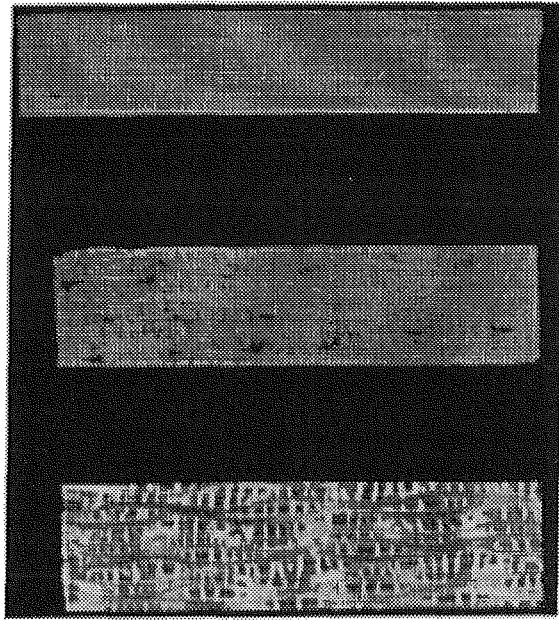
IMAGENS DE UM CORTE TRANSVERSAL DE CERÂMICA SiC (Fonte BAM)
